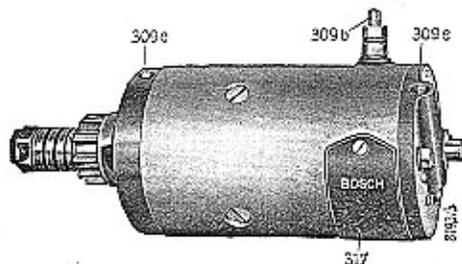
AEA-Anlasser mit Halslagerbefestigung
